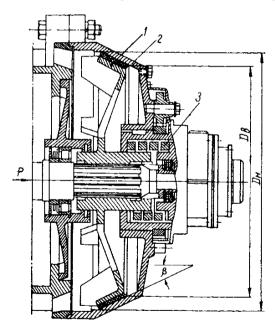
Конусный тормоз: 1 – вращающийся конус; 2 – невращающийся конус; 3 – пружина
